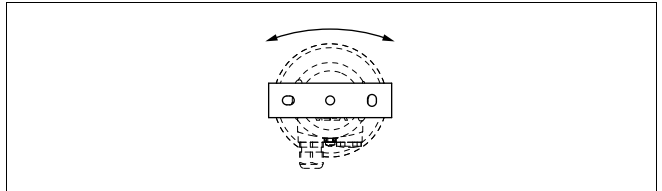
Posibilidad de giro del estribo de montaje en caso de fijación central
